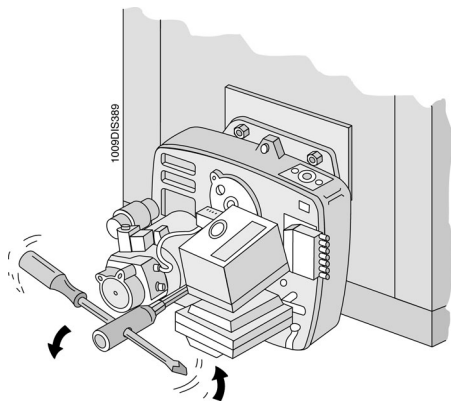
Fig. B. Destornillando el pivote de fijación de la placa se puede abrir el quemador para poder acceder al ventilador, al pulverizador, a los electrodos y al precalentador.
